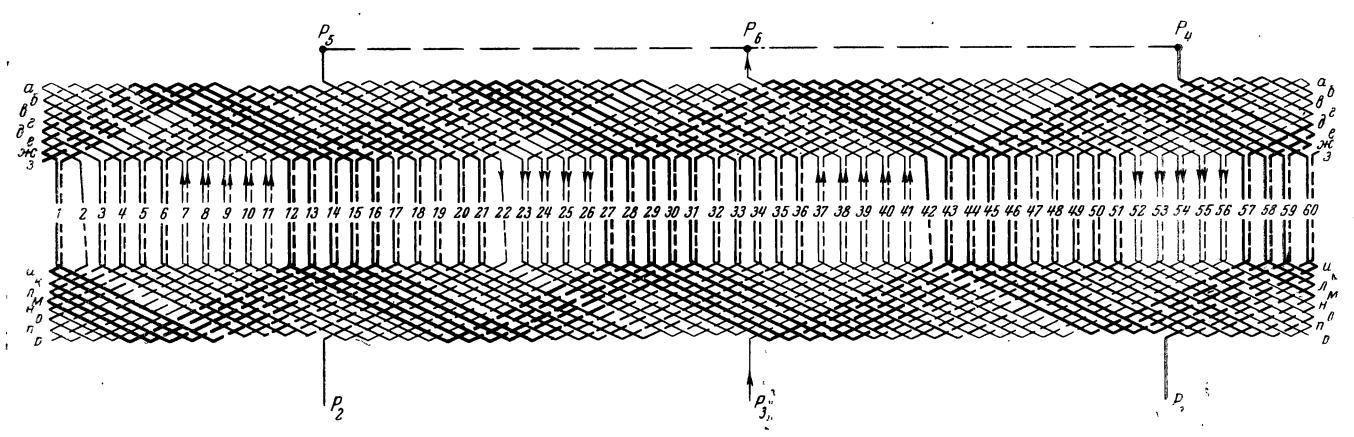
Развернутая схема двухслойной стержневой роторной обмотки при 2p=4; z=60; q=5; y=1-16; a=1. Шаг перехода укороченный 1-15. Соединение фаз χ .
